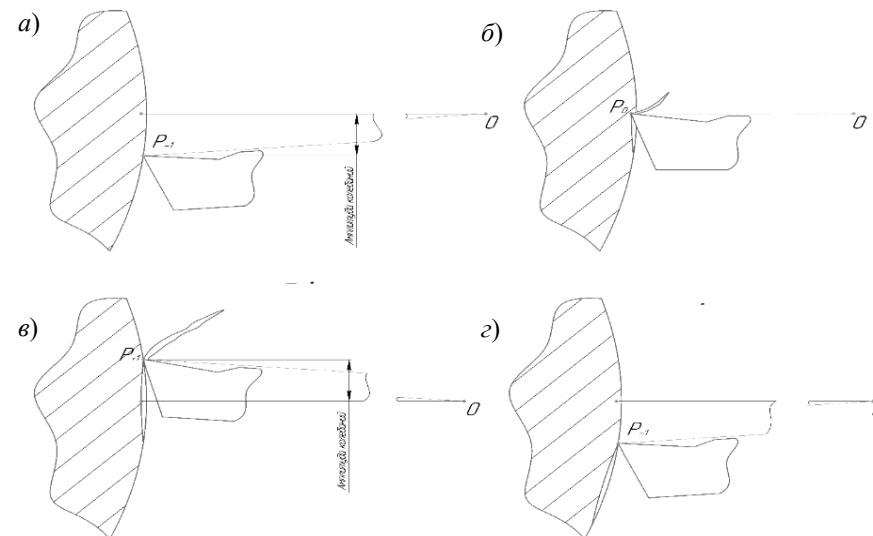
Схема колебаний режущего инструмента: *a* – нижнее положение инструмента; *б* – нейтральное положение инструмента; *в* – верхнее положение инструмента; *г* – нижнее положение инструмента (после образования профиля канавки)
